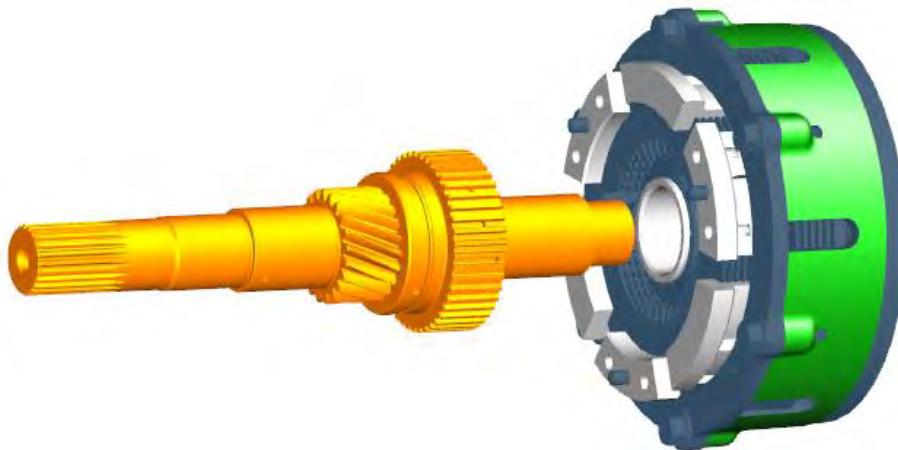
"Montaje del conjunto de embragues con eje longitudinal del eje de entrada"
